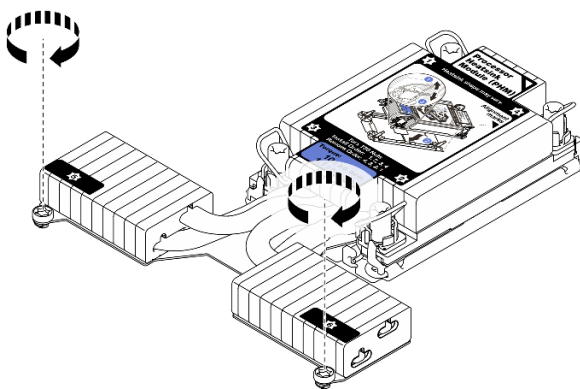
Serrage des vis du dissipateur thermique en forme de T
